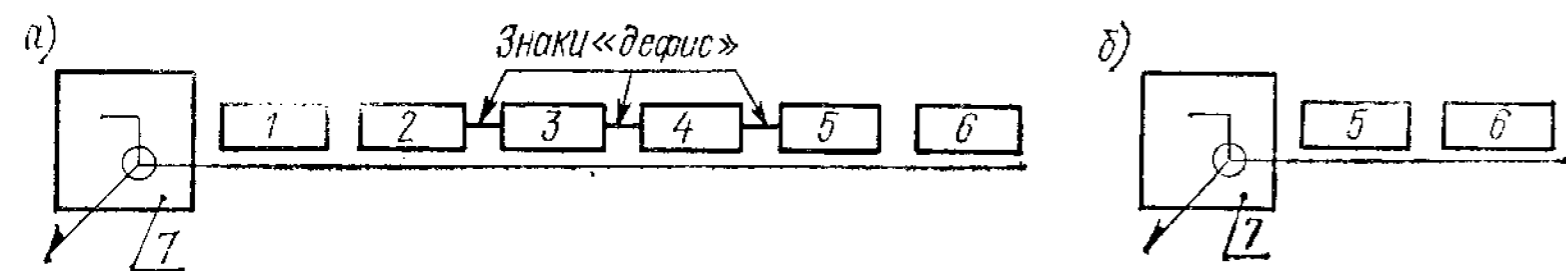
Структура условного обозначения сварного шва: а — стандартного; б — нестандартного
